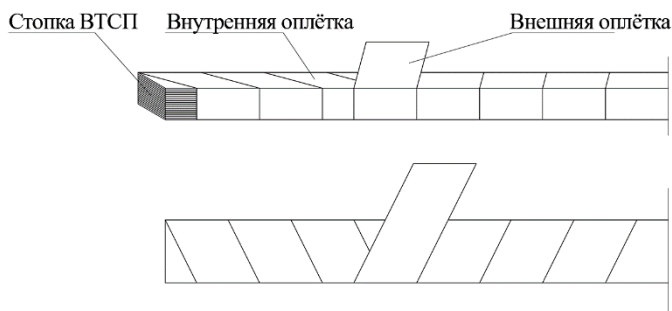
Схема образца с двухслойной плетёной оболочкой
